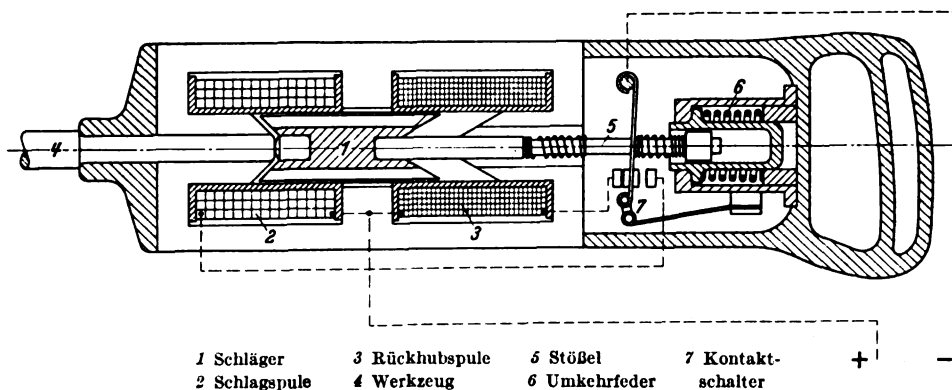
Aufbau eines Schlagwerkzeuges mit zwei Magnetspulen.
